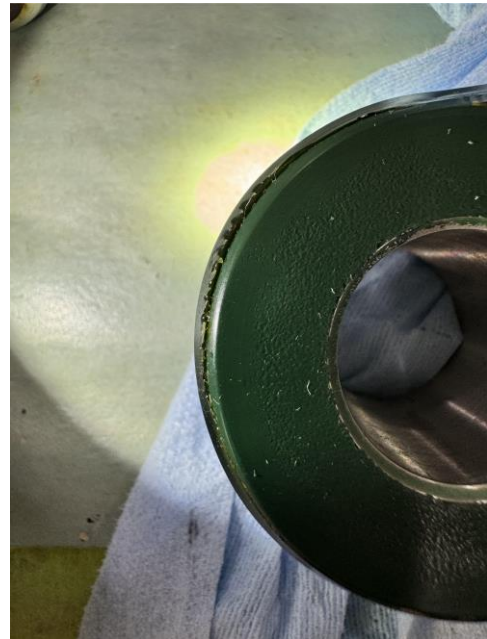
Fissure dans le revêtement d'uréthane du faisceau torsible d'Airwolf installé sur un hélicoptère Bell 206B
